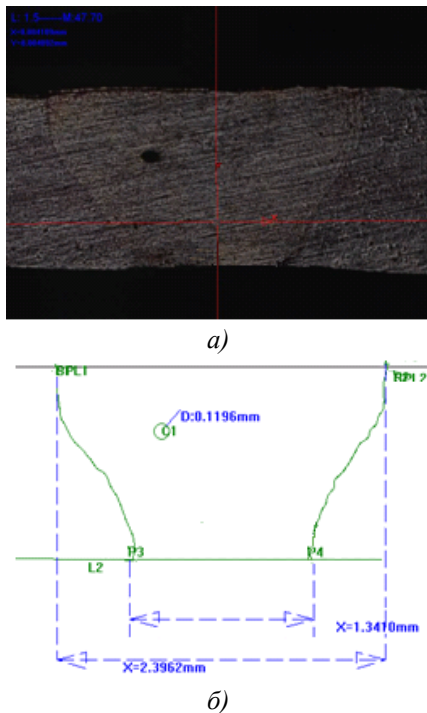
Образец стыкового сварного соединения образца сплава АД33 ручной лазерной сваркой: макроструктура  $\times 50$  (а); геометрические параметры зоны термического влияния (б)
